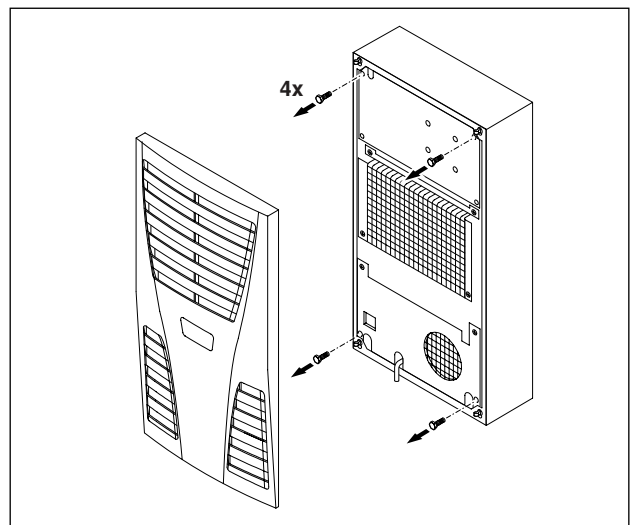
Nur SK 3302.xxx: vier Schrauben entfernen
